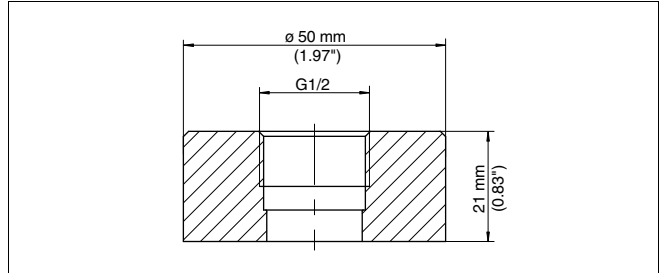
Medidas racor soldado G $\frac{1}{2}$  B según ISO 228-1 - depósito
